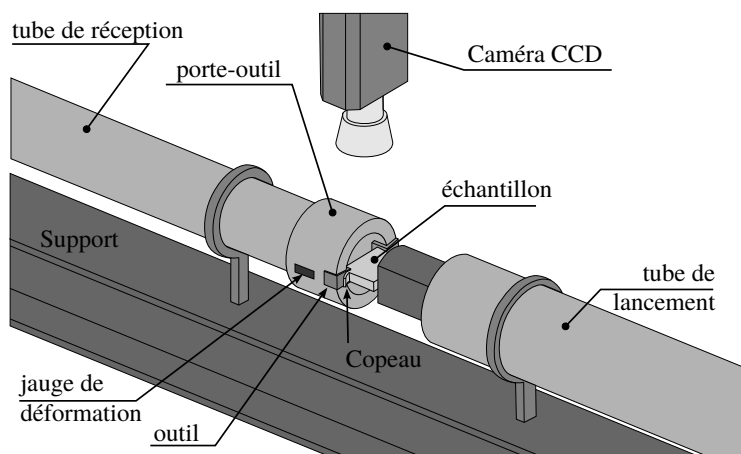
Essais de coupe pour l'acier sur barres de Hopkinson (D'après [List 13]).
